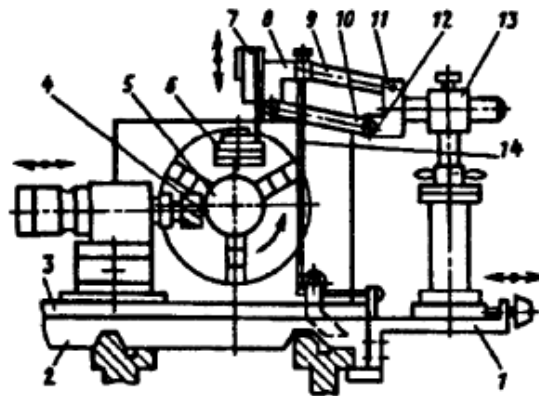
Пристрій для стабілізації довжини стисненої дуги: 1, 8, 13 - кронштейни; 2 - супорт; 3 - санки; 4 - фреза; 5 - заготовка; 6 - пальник; 7 - вібратор; 9,10 - тяги; 11,12 - пружини; 14 - трос.
